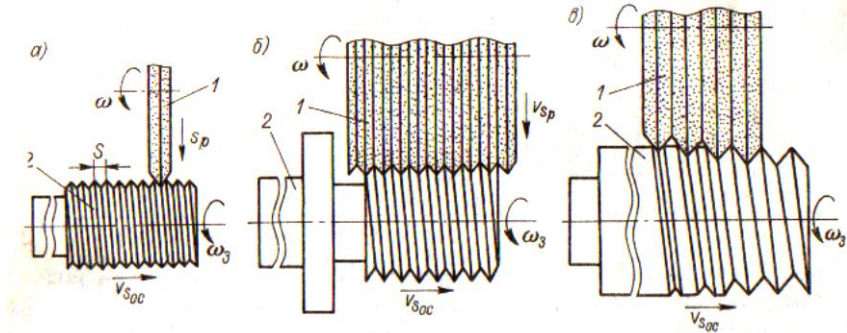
Схема резьбошлифования: 1 – шлифовальный круг; 2 - заготовка
